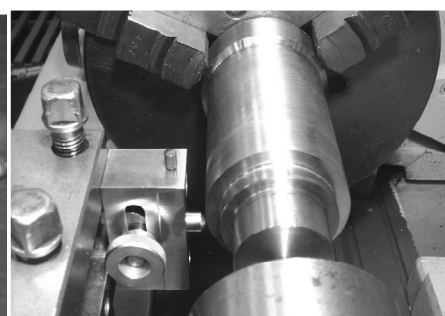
Фотография обработки детали насоса алмазным выглаживанием на токарном станке
